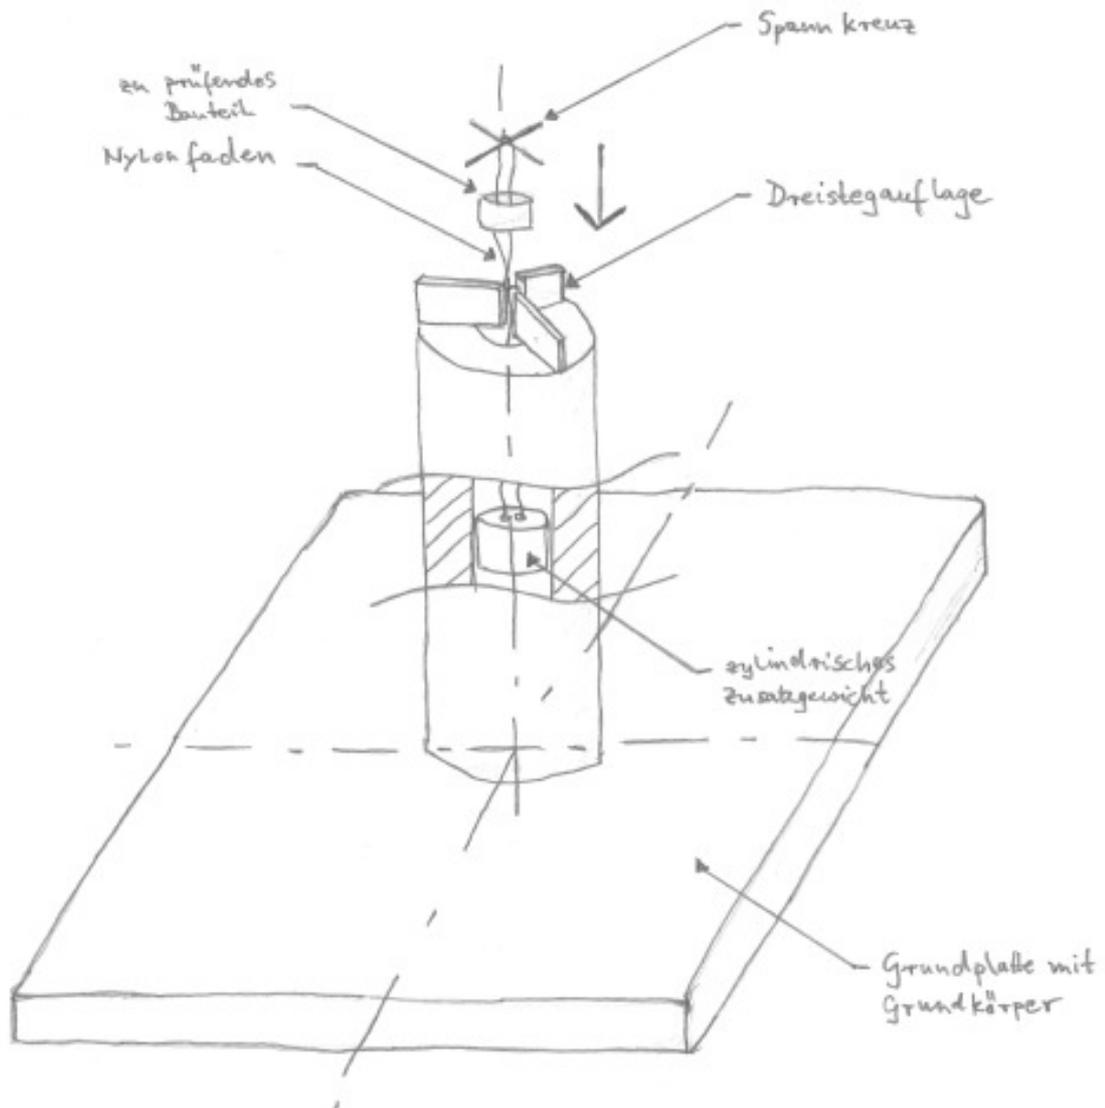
Prinzipskizze LV 3. Die Vorrichtungsbaulemente sind auf einer Grundplatte angeordnet. Die Spannkraft wird durch ein Zusatzgewicht in Zylinderform erzeugt. Die Spannkraft kann durch das Gewicht des Zylinders bestimmt werden und gerade so groß gewählt werden, wie für eine stabile Fixierung des zu prüfenden Bauteils nötig ist. Ein Nylonfaden verbindet das Zusatzgewicht und das Spannkreuz, welches das Bauteil auf einer Dreistegauflage fixiert. Der Nylonfaden wird, bedingt durch die Geometrie des Spannkreuzes, zentriert. Die Spannkraft wird nah an der Bauteilauflage und senkrecht zu dieser eingeleitet. Die Vorrichtung kann zum größten Teil additiv mit Kunststoff gefertigt werden. Das Zusatzgewicht sollte aus einem Material höherer Dichte, wie beispielsweise Stahl sein. Die Stege und das Spannkreuz aus Kunststoff schonen die Flächen des zu spannenden Bauteils.
